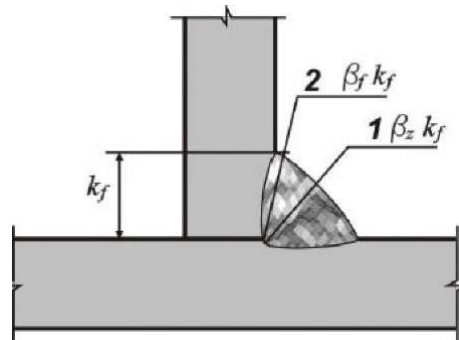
Схема расчетных сечений сварных соединений С угловыми швами.
